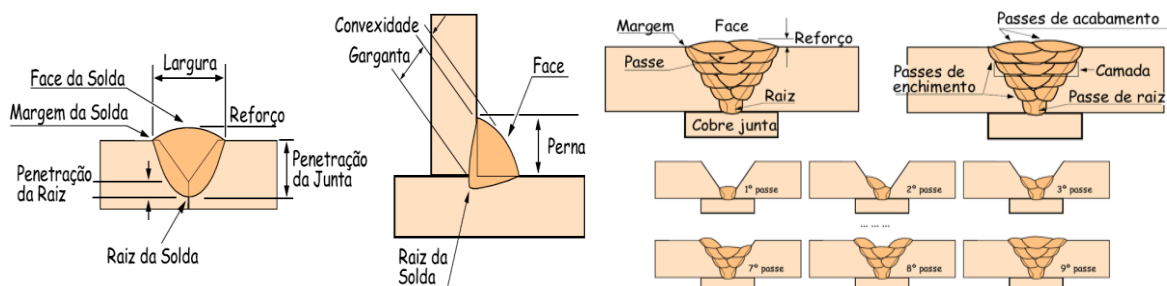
Elementos de uma junta soldada. (Fonte: Soldagem: fundamentos e tecnologia / Paulo Villani Marques, Paulo José Modenesi, Alexandre Queiroz Bracarense – 3ª edição atualizada – Belo Horizonte: Editora UFMG, 2009)
